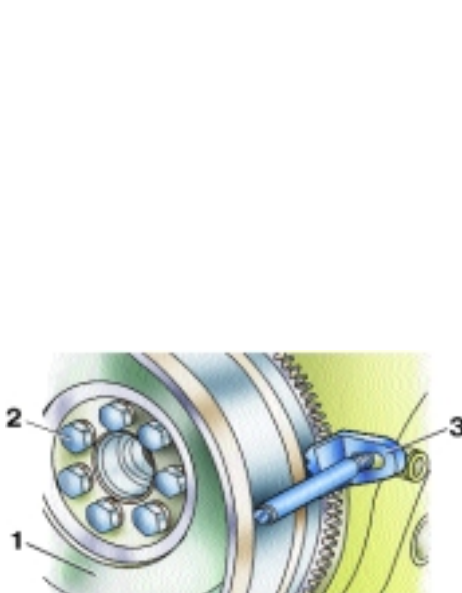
Крепление маховика двигателя F3R 272: 1 – маховик; 2 – болт крепления маховика; 3 – приспособление для фиксации маховика
